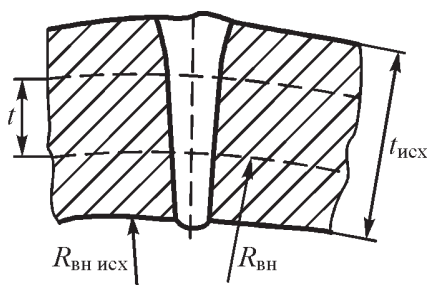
Вид сварного соединения из сплавов типа АМг6Н и АМг6НПП, выполненного электронно-лучевой сваркой
